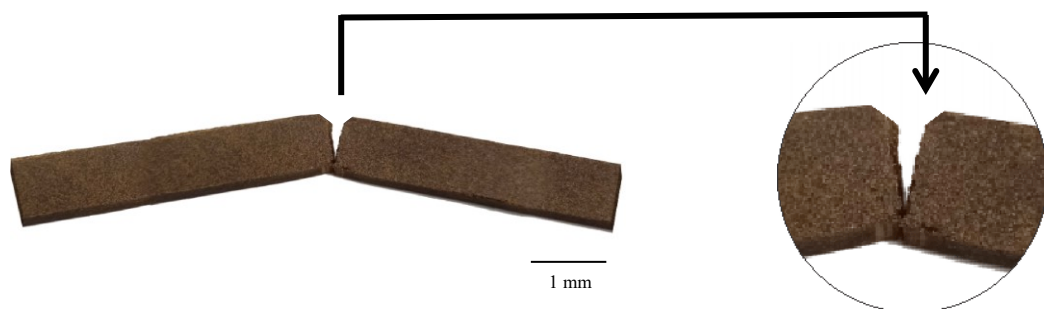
Corpo de prova para ensaio de impacto Izod: a) Corpo de prova padrão de flexão com fratura após o ensaio e b) detalhe da fratura.
